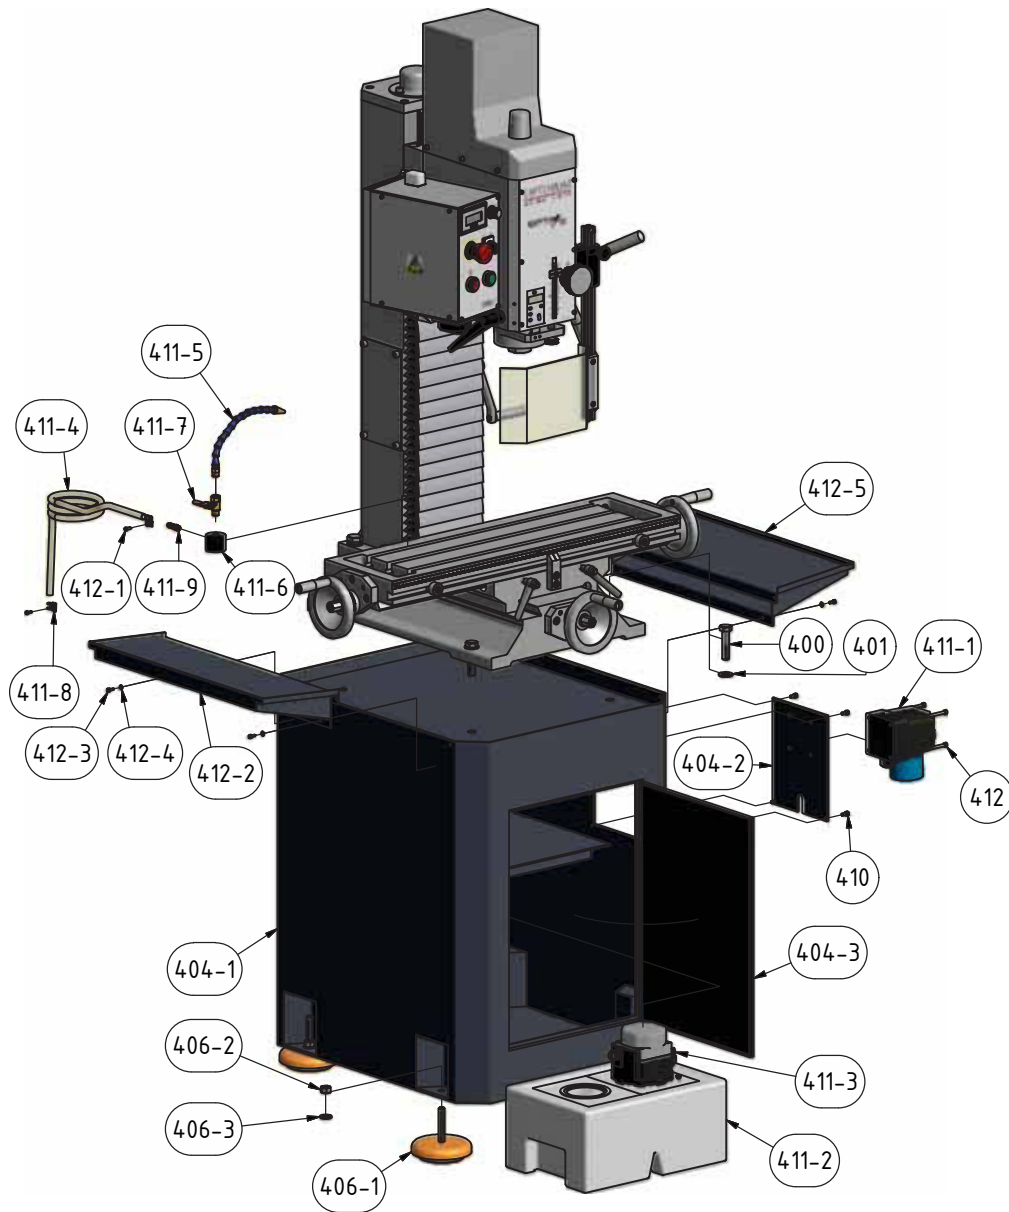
Maschinenunterbau (optional)- Machine stand (option)
